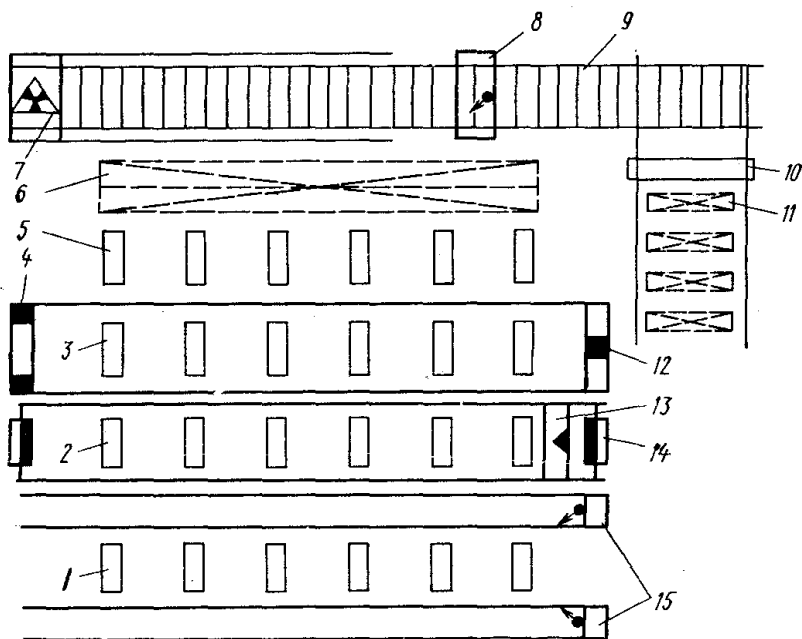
Схема поточной линии изготовления балок коробчатого сечения
